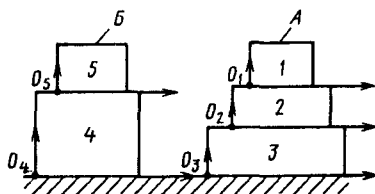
Конструкция сборочной единицы из пяти деталей
